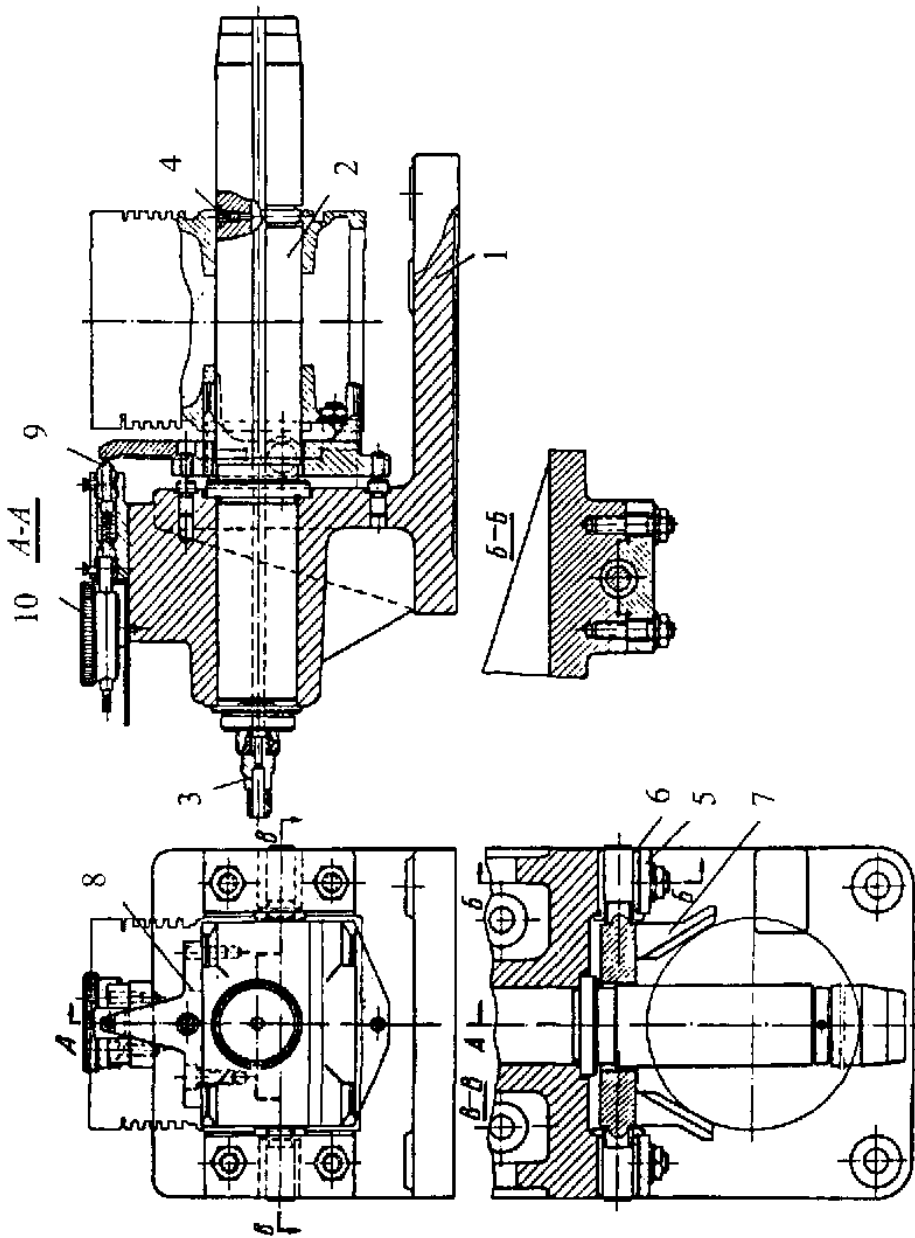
Комбінований пневматичний та індикаторний пристрій для контролю поршня
